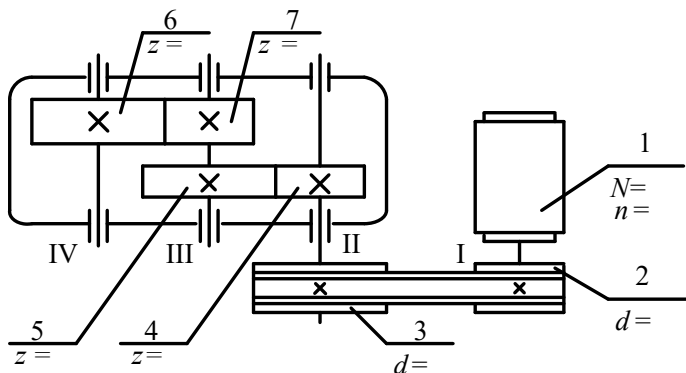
Кинематическая схема привода с двухступенчатым цилиндрическим редуктором и ременной передачей:
